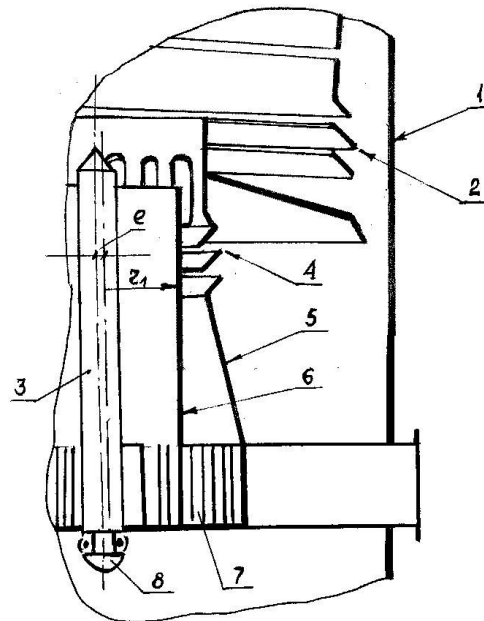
Конструктивне оформлення первинного завихрителя: 1 – корпус; 2 – жалюзійний розвантажувач сепараційної камери; 3 – осьовий витиснювач; 4 – жалюзійний розвантажувач первинного завихрувача; 5 – конфузор; 6 – циліндр; 7 – вертикальні жалюзі; 8 – шарнір.
